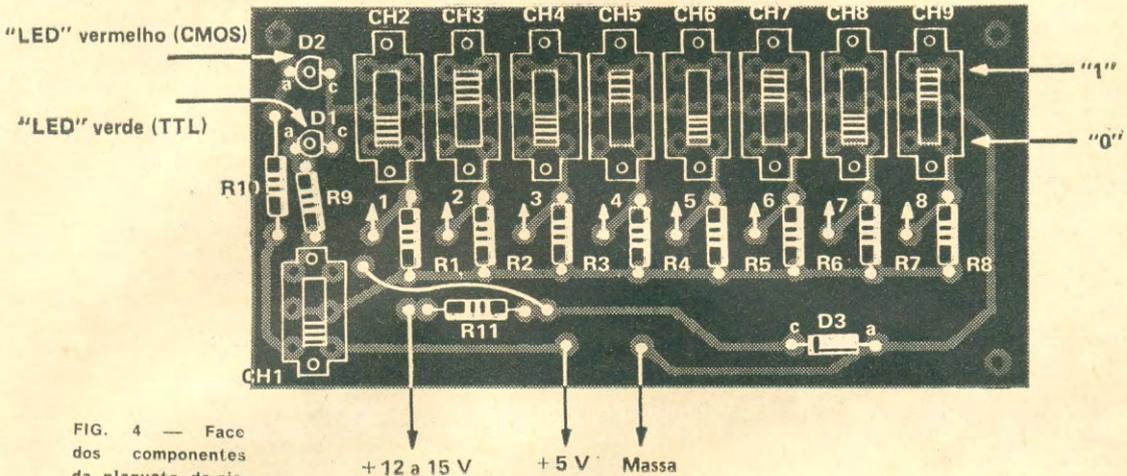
Face dos componentes da plaqueta de circuito impresso.
